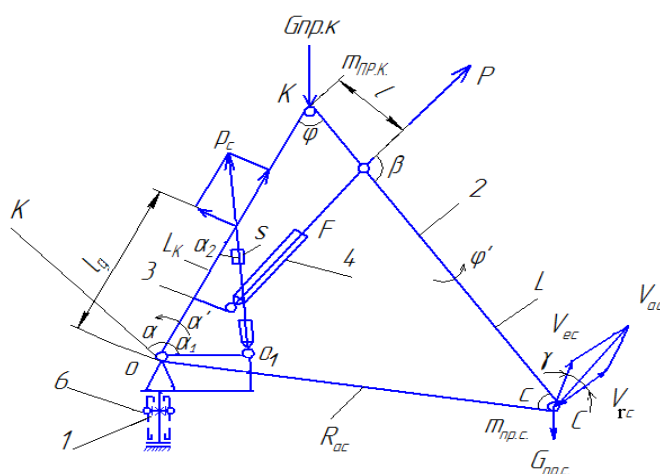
Расчетная схема системы «технологическое оборудование – груз» (манипулятор с отклоняющейся колонной): 1 – опорно-поворотное устройство; 2 – стрела; 3 – колонна; 4 – гидроцилиндр подъема стрелы; 5 – гидроцилиндр
